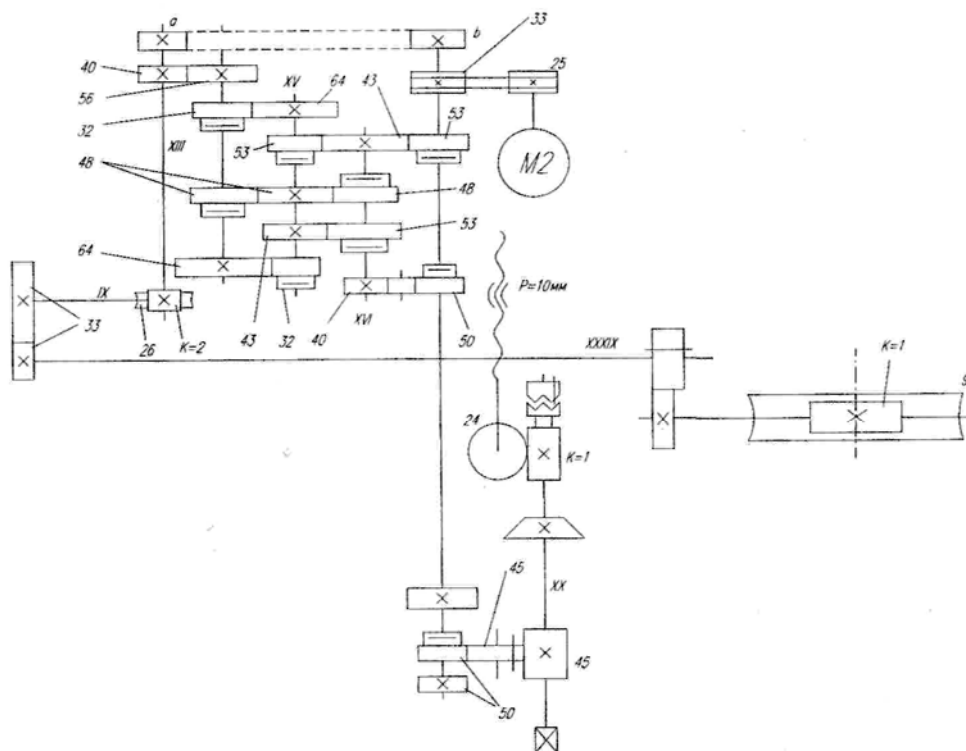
Кинематическая схема цепи вертикальной подачи фрезы станка 5К324
